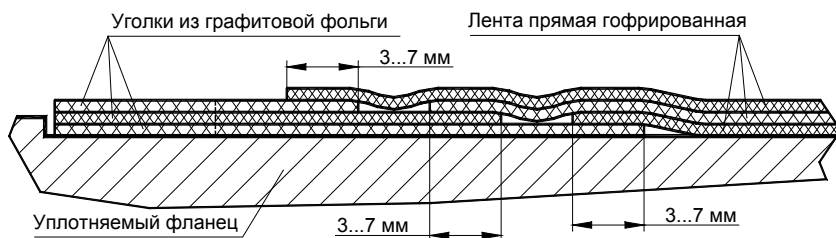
Прокладка прямоугольная (вариант).
